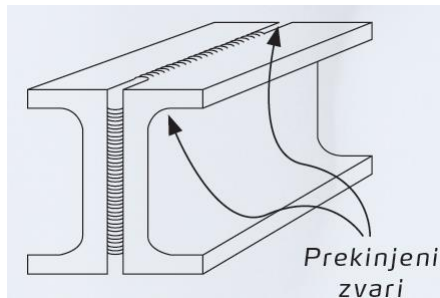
Zwei Profilen muss nicht dicht zueinander verschweißt wegen Korrosion
